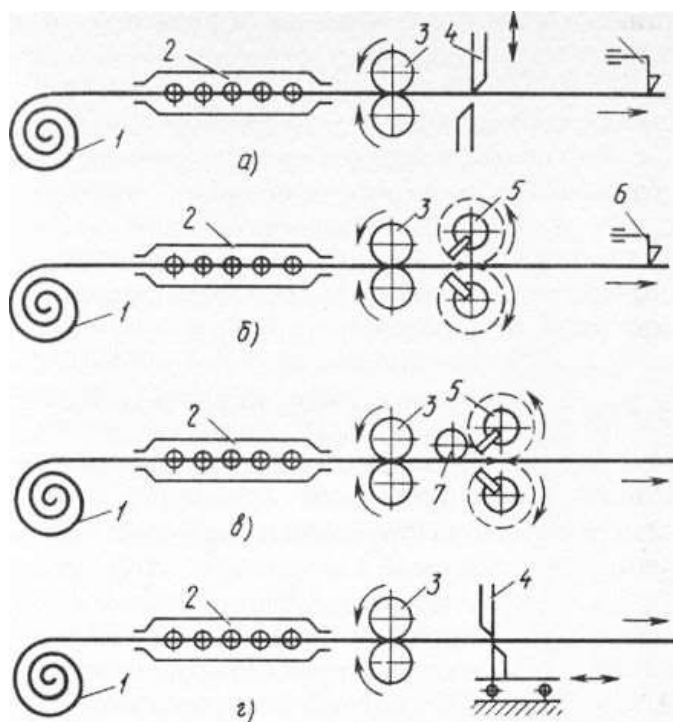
Принципиальные схемы правильно-отрезных станков с рычажными ножами и концевым выключателем (а), с вращающимися ножами и концевым выключателем (б), с вращающимися ножами и мерительным роликом (в), с летучими ножами и концевым выключателем (г): 1 – вертушка, 2 – барабан правки, 3 – подающие ролики, 4, 5 – ножи, 6 – концевой выключатель, 7 – мерительный и прижимной ролики
